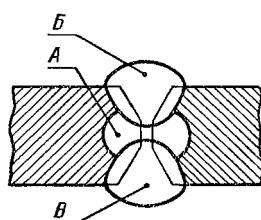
Обозначение многопроходного шва сварного соединения
